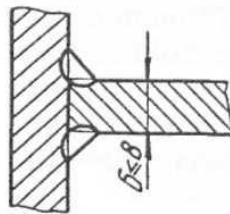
Вид зварного з'єднання лапи з плитою.
